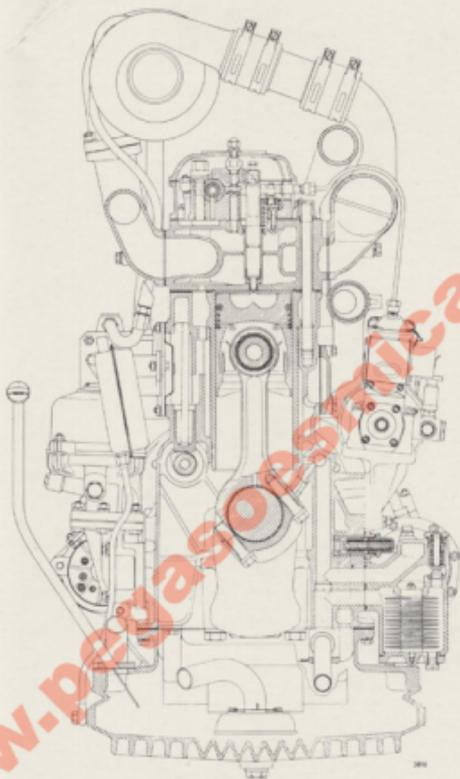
Motor 9156 y derivados. Sección transversal (Montaje HASTA)
